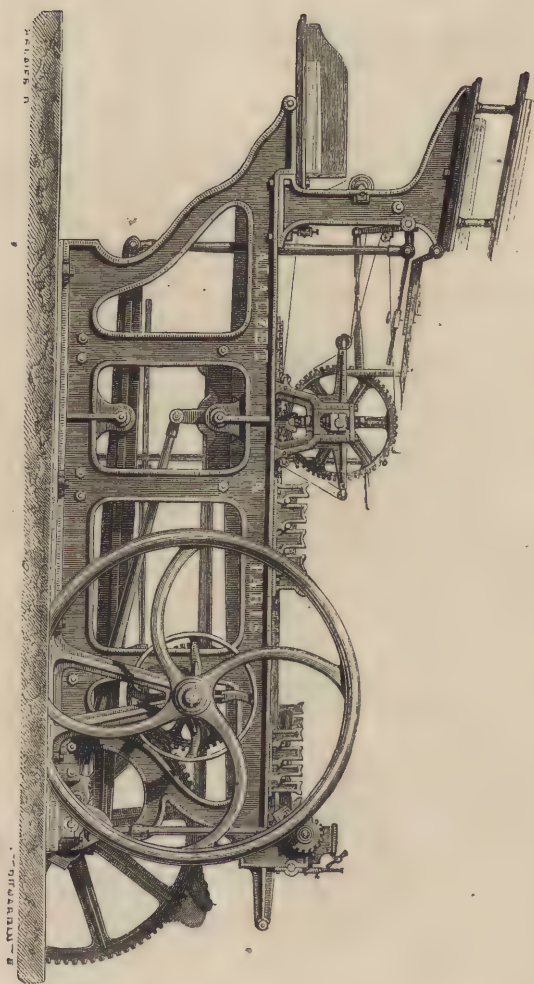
MACHINE EN BLANC, DITE « UNIVERSELLE ».
